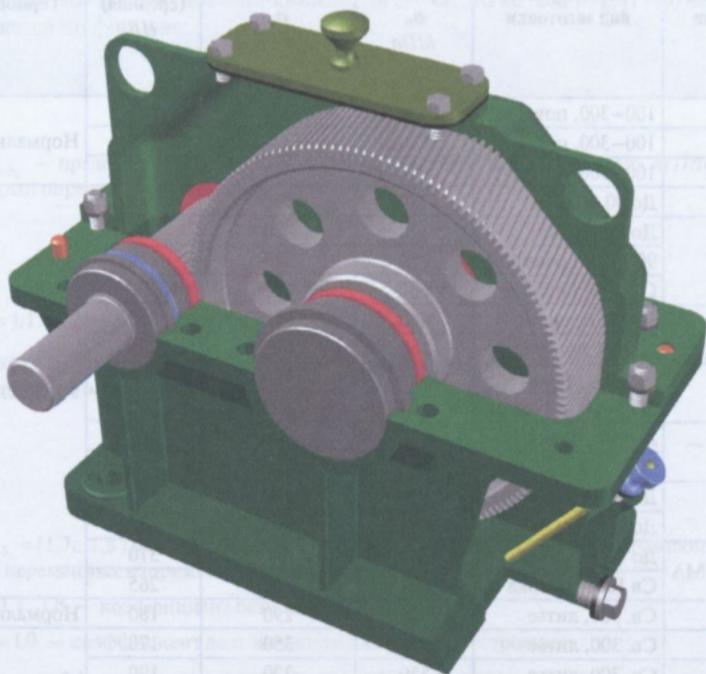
Редуктор цилиндрический одноступенчатый
